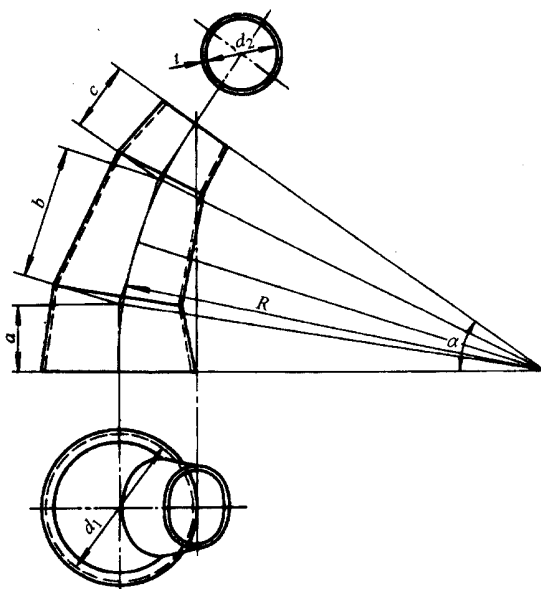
圆锥管三节任意角度弯头的主视图和俯视图
